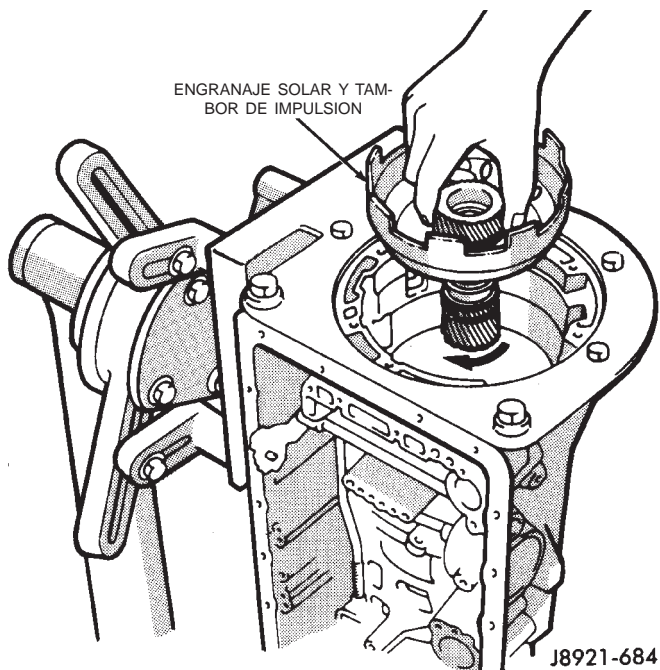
Instalación del engranaje solar y el tambor de impulsión
